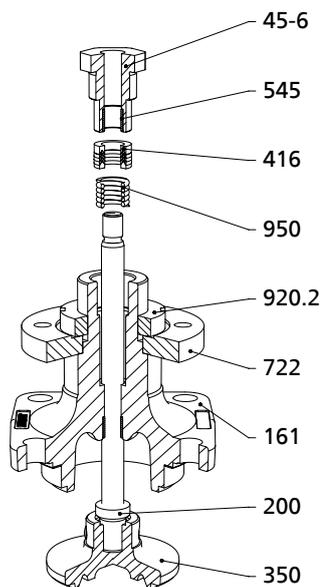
Desmontaje de la junta con perfil en V de PTFE
